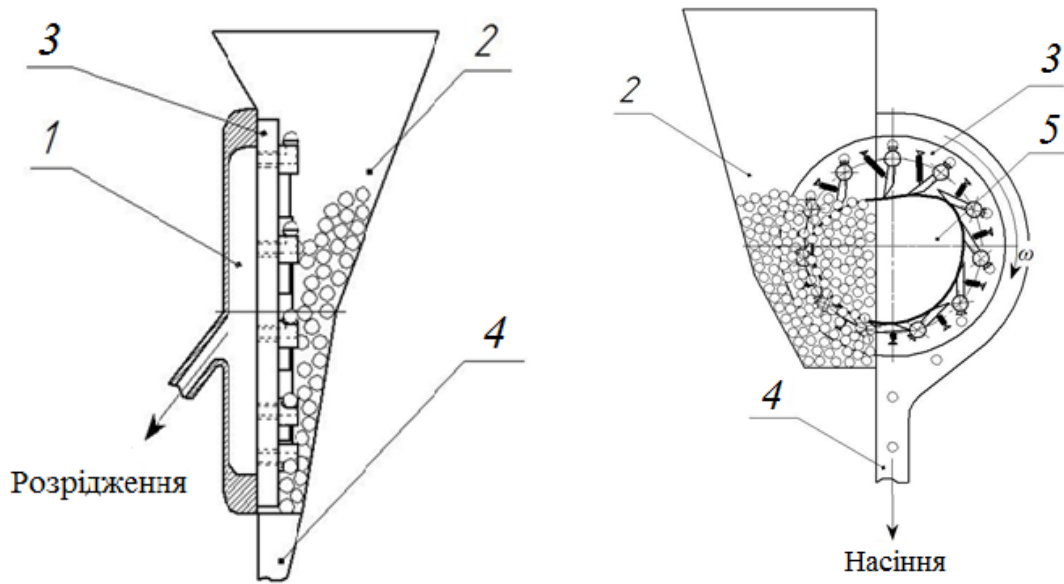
Пневмомеханічний висівний апарат з дозатором направленої дії: 1 – вакуумна камера; 2 – насіннева камера; 3 – висівний диск; 4 – насіннепровід; 5 – копір.
